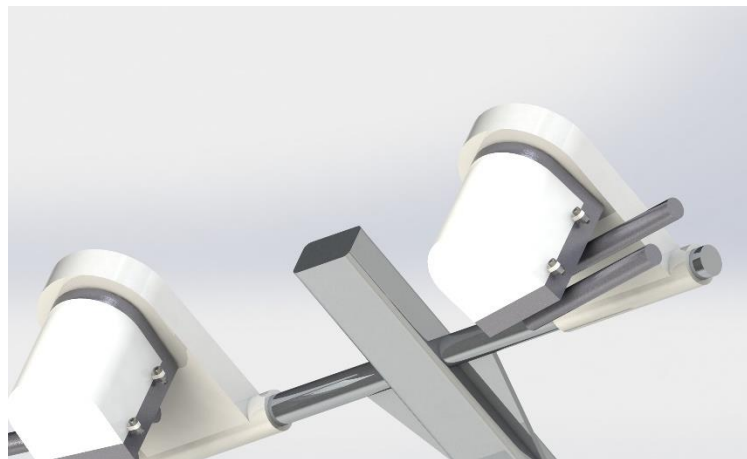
Imagen de detalle de carcasa ensamblada.
